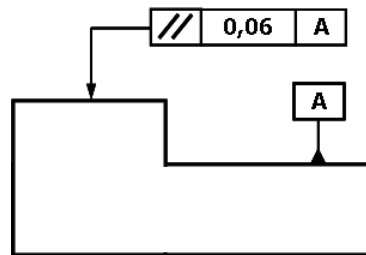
Indicação de tolerância de paralelismo em desenho técnico
